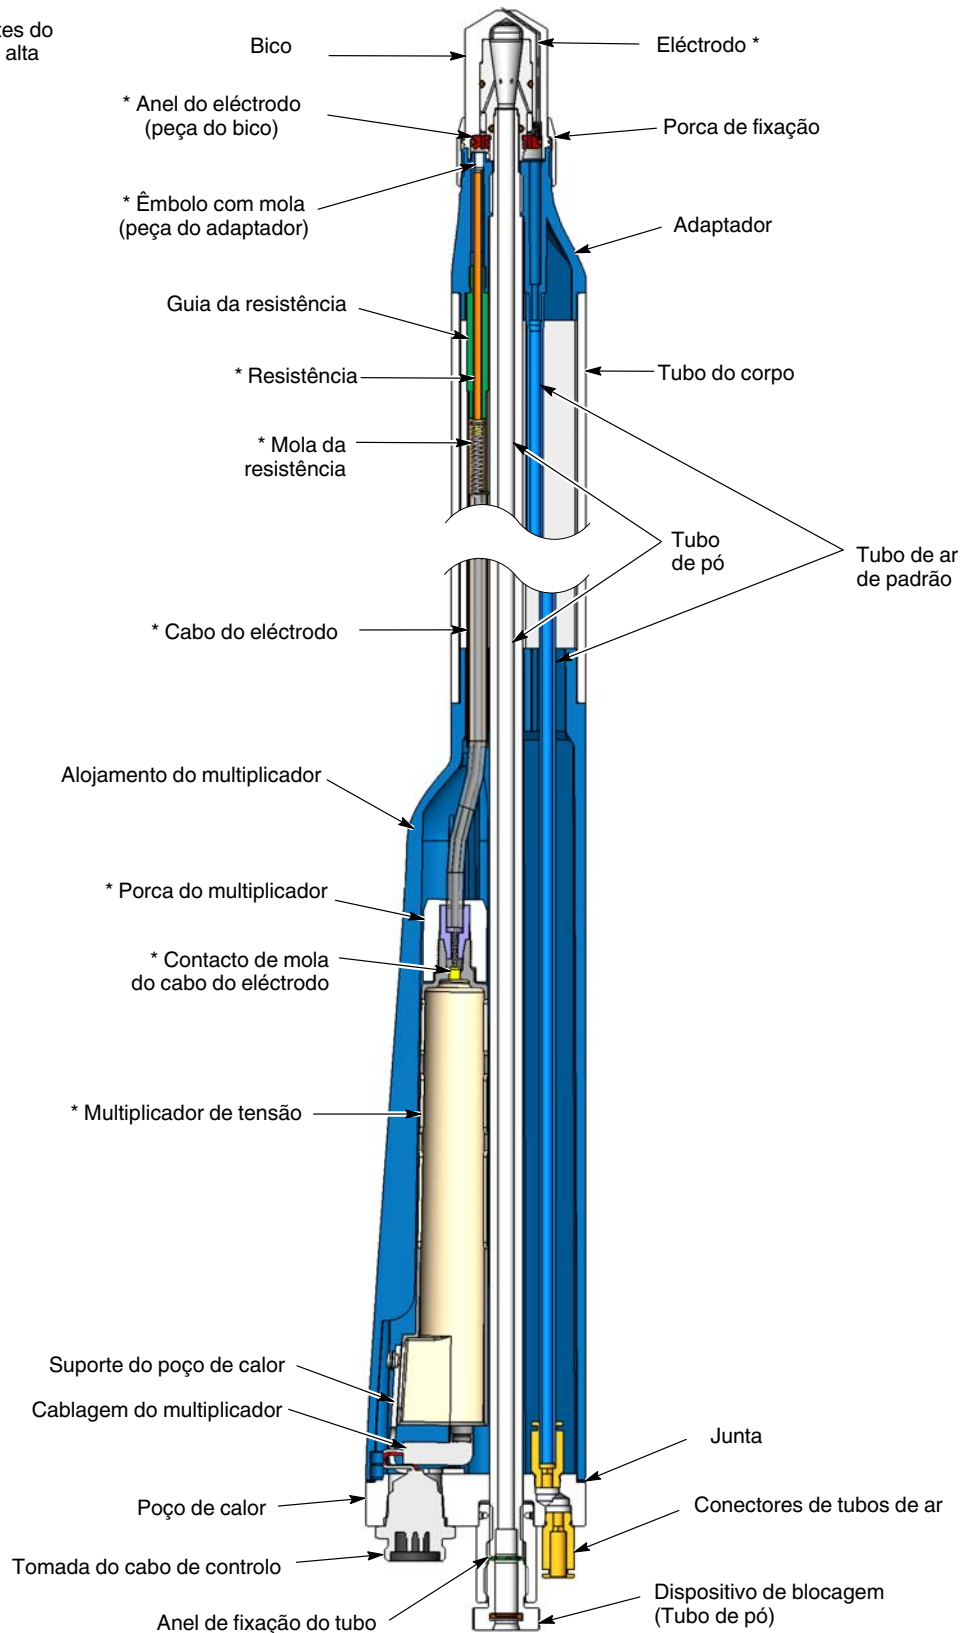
Vista em corte - Componentes e montagem da pistola com tubo de suporte
